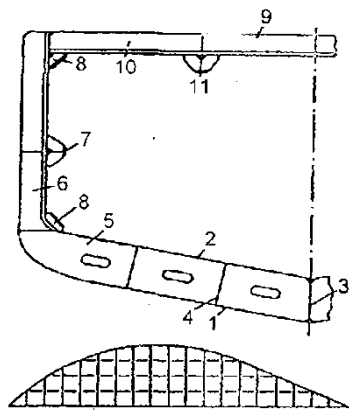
Схема набора днища и конструктивный мидель-шпангоут корабля, набранного по поперечной системе: 1 – наружная обшивка; 2 – настил второго дна; 3 – вертикальный киль; 4 – стрингер; 5 – флор; 6 – бортовая шпангоутная стойка; 7 – бортовой стрингер; 8 – кница; 9 – палубный настил; 10 – бимс; 11 – карлинг
